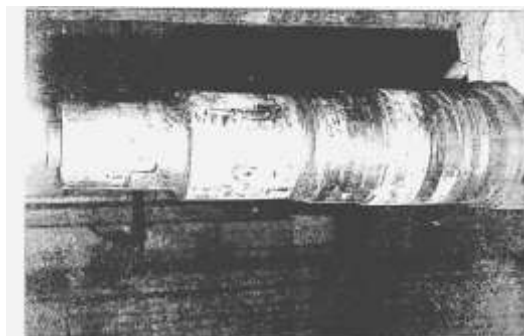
Корозійно-абразивний знос підшипників шийок вала ротора насоса НС-180
